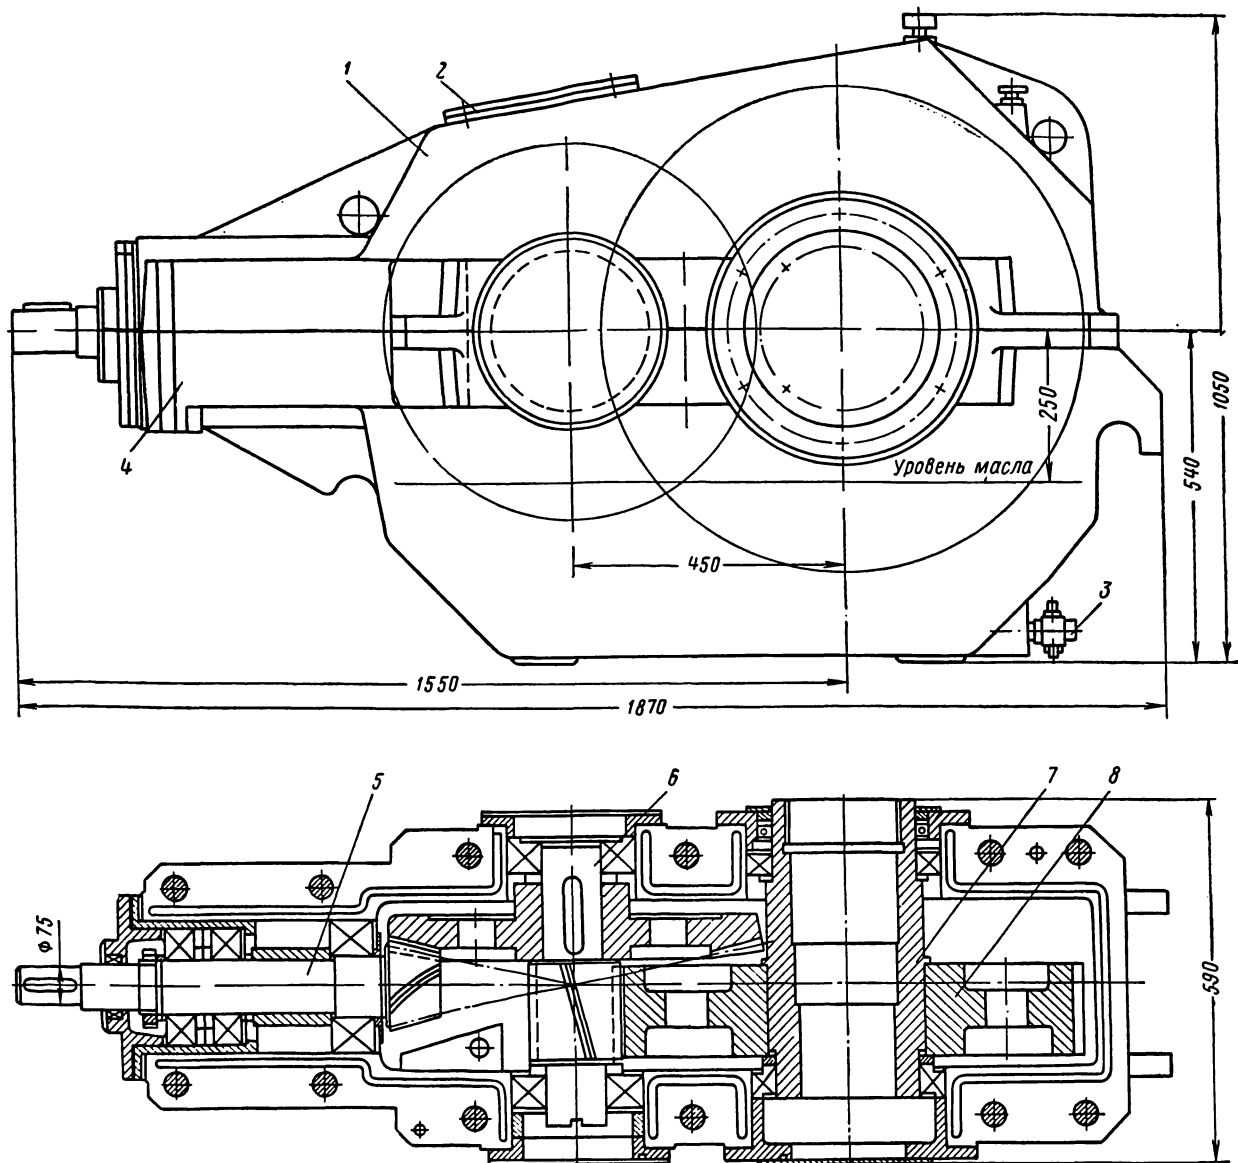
Редуктор цилиндрикоконический двухступенчатый КЦП-450:
